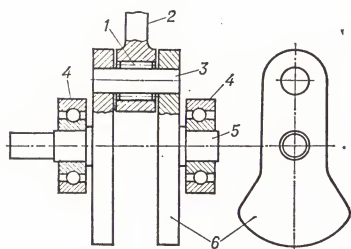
Подшипниковый узел составного коленчатого вала: 1, 4 — подшипники качения; 2 — шатун; 3 — шатунная шейка; 5 — коренная шейка; 6 — противовес.
